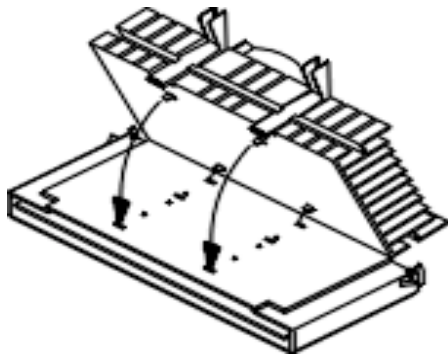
Instalowanie mechanizmu mocującego procesor
